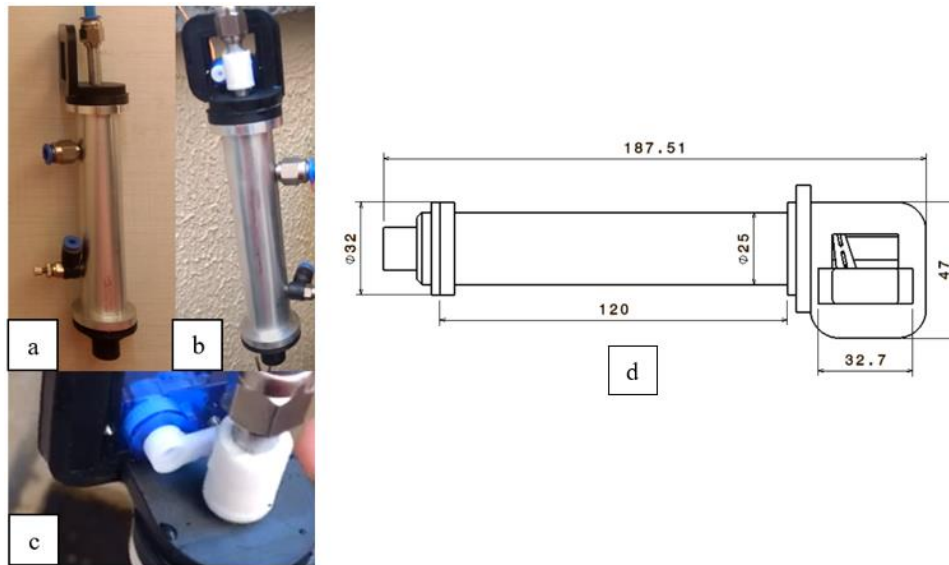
Válvula acabada com detalhe do servo. (a) Vista frontal. (b) Vista lateral. (c) Detalhe da montagem do mecanismo atuador do servomotor. (d) Dimensões principais do produto acabado (Dados dos autores)
